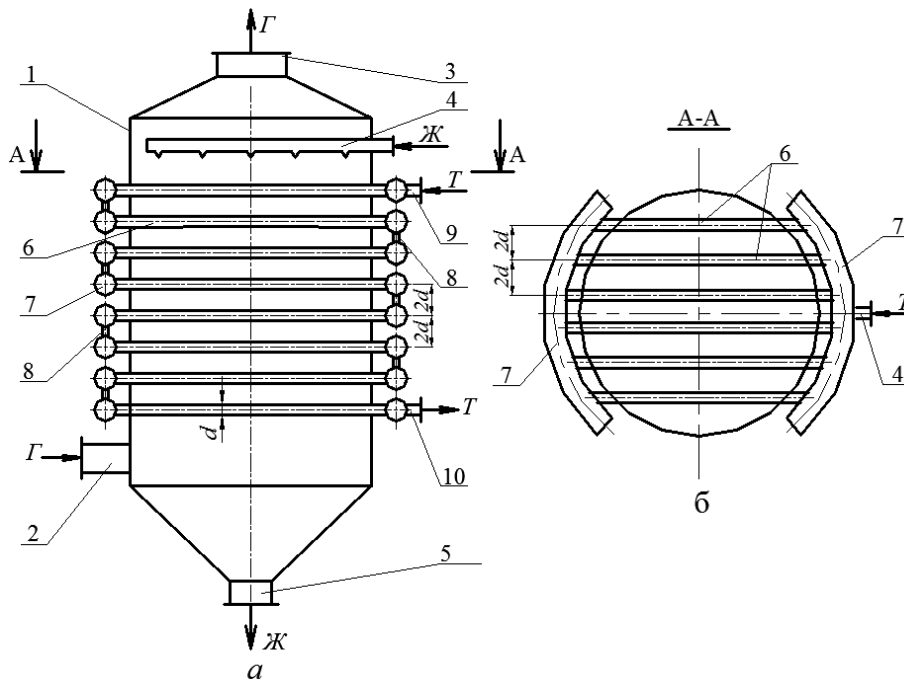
Аппарат с трубной насадкой: 1 – корпус; 2 и 3 – штуцеры для ввода и вывода газа; 4 – ороситель; 5 – патрубок для слива отработанной жидкости; 6 – трубы; 7 – коллекторы; 8 – соединительные штуцеры; 9 – патрубок подачи теплоносителя; 10 – патрубок слива теплоносителя
